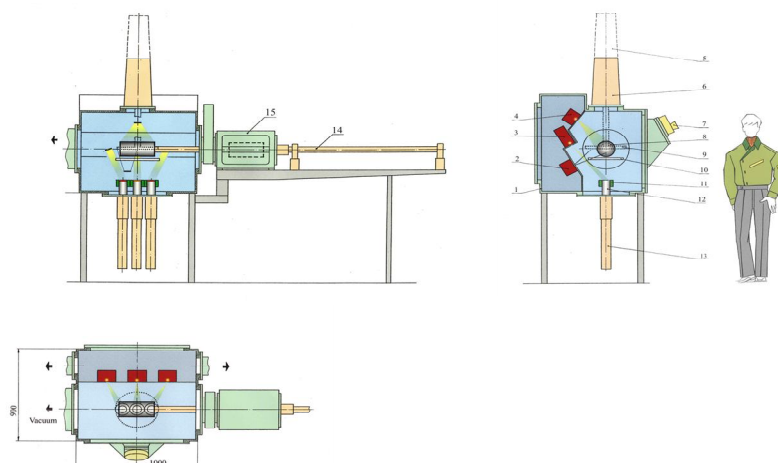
Схема технологического процесса плавки и испарения материалов в вакууме: 1 – рабочая камера; 2 – ЭЛ пушка для нагрева изделия снизу; 3 – ЭЛ пушка для испарения материалов; 4 – ЭЛ пушка для нагрева изделия сверху; 5 – вертикальный механизм для сплавления заготовки; 6 – механизм подвески и вращения изделия; 7 – смотровая система; 8 – габарит цилиндрического изделия; 9 – габарит дискового изделия; 10 – заслонка; 11 – тигель; 12 – слиток; 13 – механизм подачи слитка на испарение; 14 – горизонтальный механизм подачи изделия; 15 – шлюзовая камера
